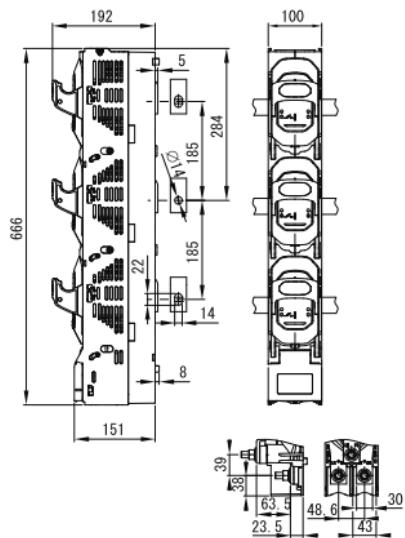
Габаритные размеры ПВР-3 250 – 630 А / Figure A.4 – Overall dimensions of PVR-3 250 – 630 A
